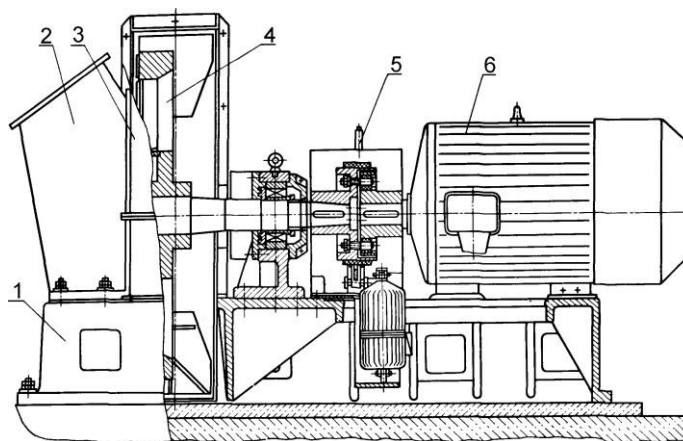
Загальний вигляд дискового подрібнювача деревини: 1 – станина; 2 - завантажувальний патрон; 3 – кожух; 4 – ротор; 5 - гальмо; 6 – електродвигун
